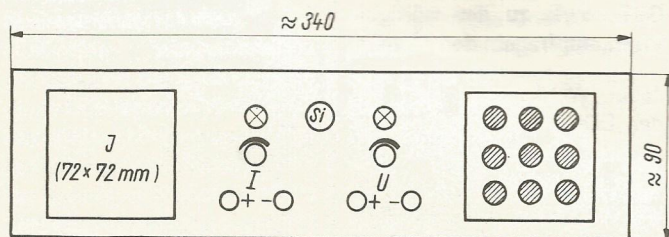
Vorschlag für die Gestaltung der Frontplatte
